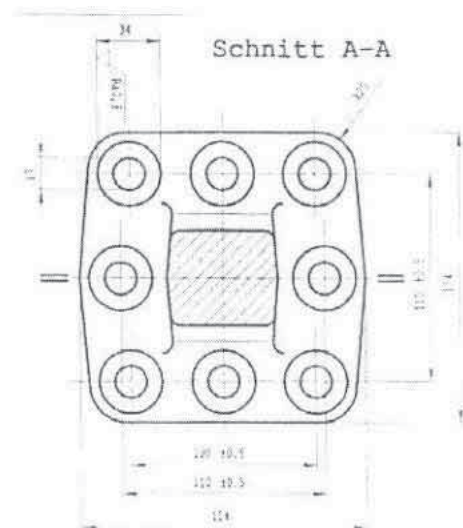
Zugöse Ausführung 1 mit 8 Loch Flanschbefestigung
